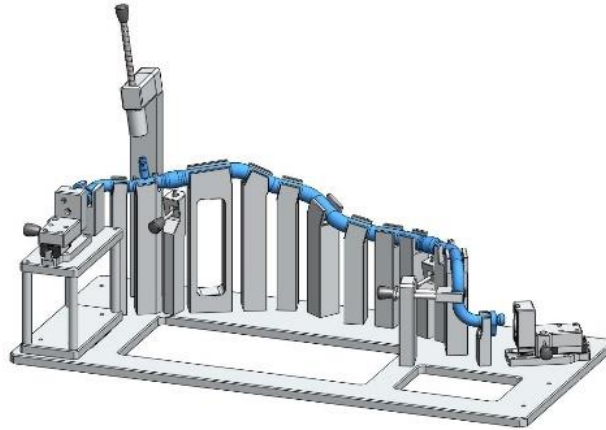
Pequeno dispositivo de controlo dimensional [39]
